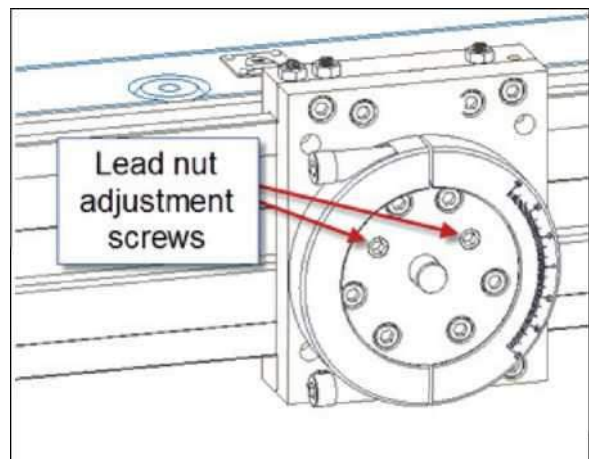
Ort der Justierschrauben der Führungsmutter
